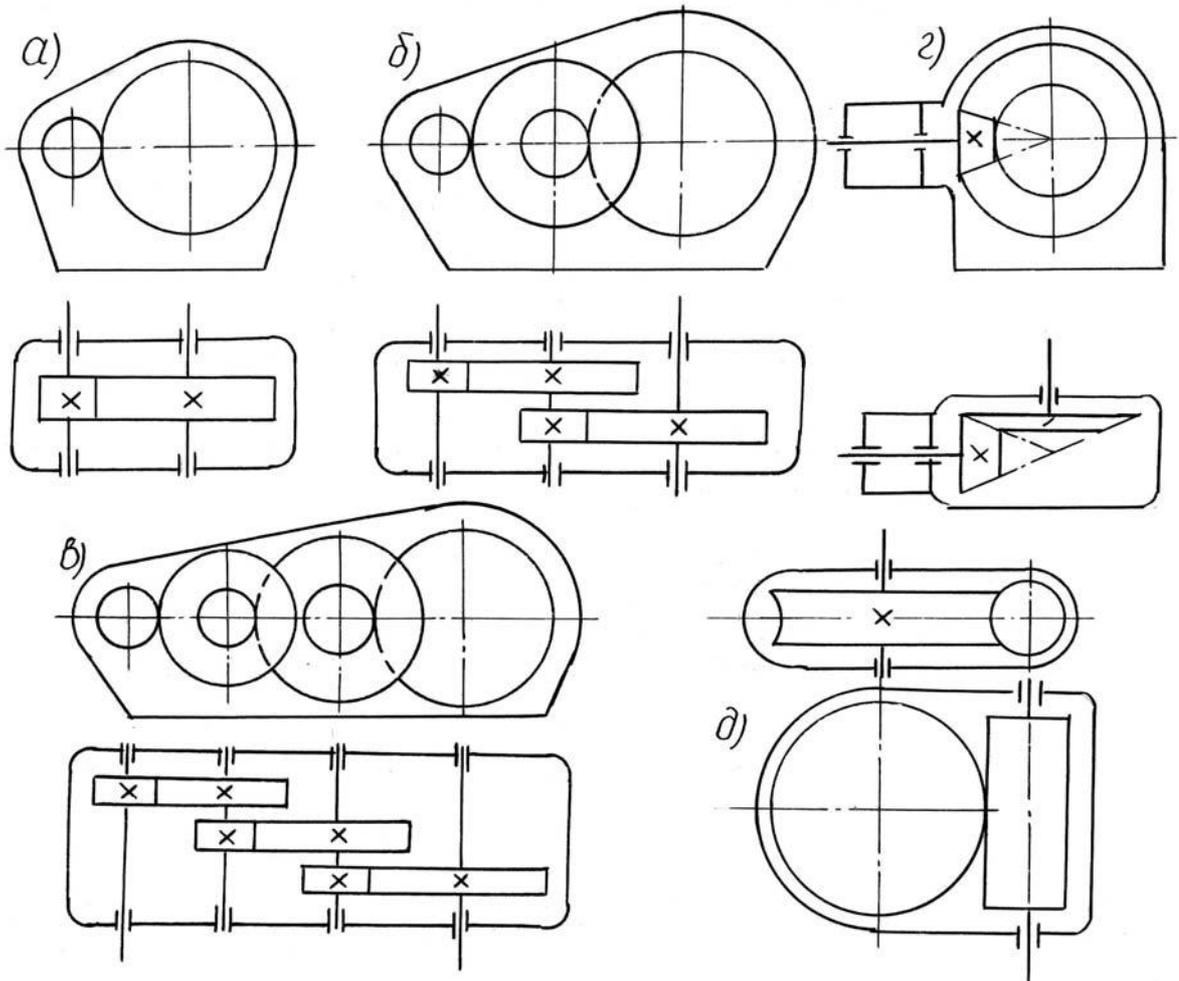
Кинематические схемы редукторов: а– цилиндрический одноступенчатый; б– цилиндрический двухступенчатый; в– цилиндрический трёхступенчатый; г – конический; д – червячный
